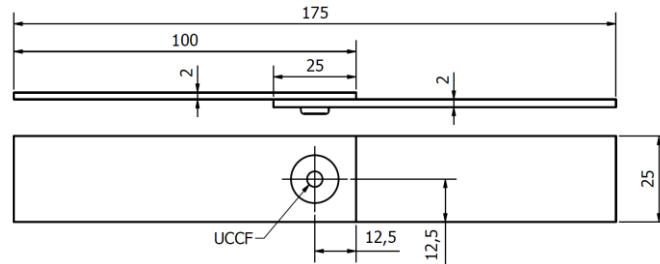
Dimensões do corpo de prova (detalhamento fornecido pela TOX)
